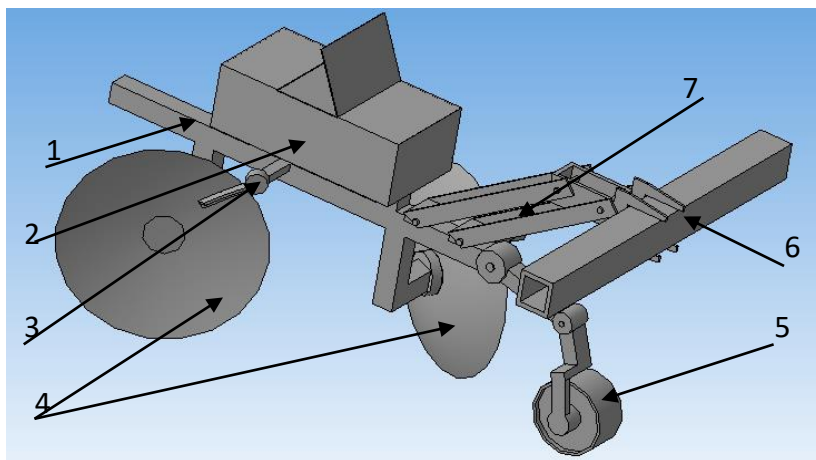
Общий вид предлагаемой конструкции окучника:
